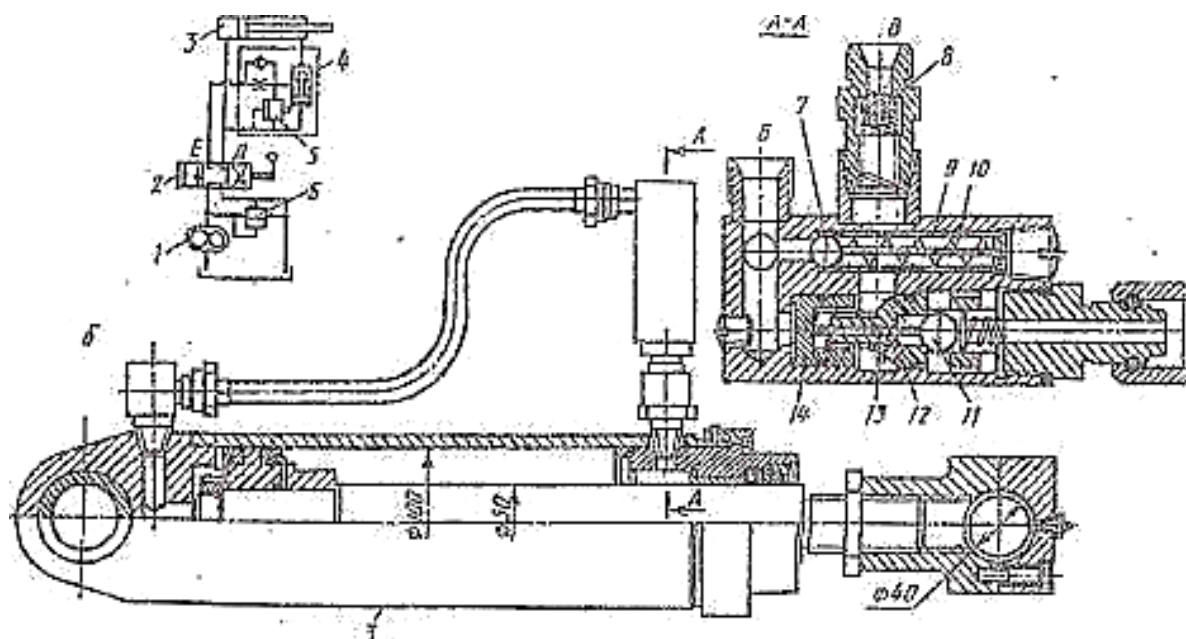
Принципиальная схема гидропривода грузоподъемного борта (а) и конструкция гидроцилиндра (б) с гидрозамком: 1 – шестеренный насос; 2 – золотниковый распределитель; 3 – гидроцилиндр; 4 – гидрозамок; 5, 6 – предохранительный клапан; 7 – шарик; 8 – дроссель; 9 – крестовина; 10 – пружина; 11 – шарик; 12 – седло; 13 – игла; 14 – поршень гидрозамка; Б, В, Г – полость; Д, Е – канал
